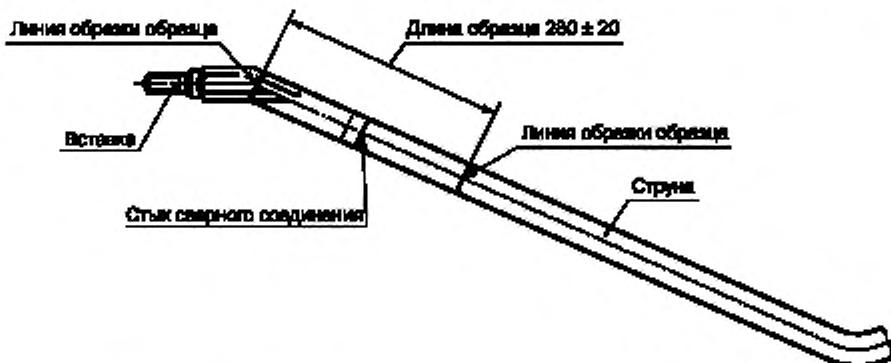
Схема вырезки образца для испытания сварного соединения, выполненного контактной стыковой сваркой
